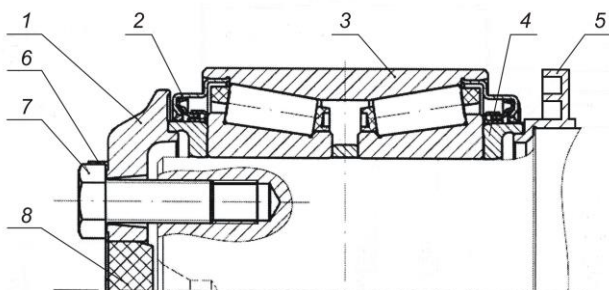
Вариант исполнения конического подшипникового узла, применяемого в корпусе буксы:
